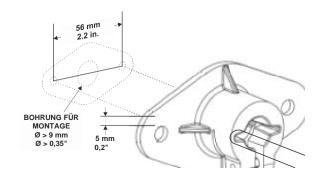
Flanschmontage an Kanal (mm, Zoll)
